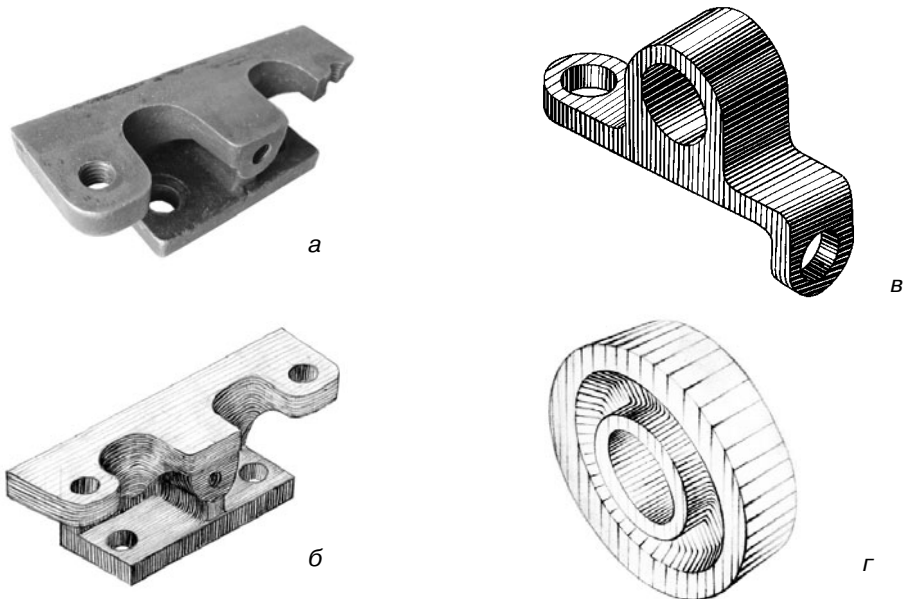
Выявление плавных переходов поверхностей способом штриховки:
